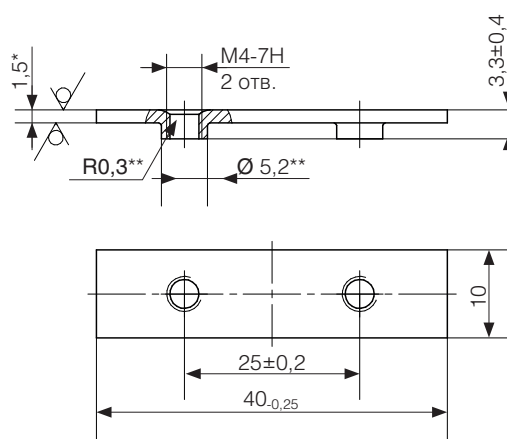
Габаритные, установочные и присоединительные размеры МВЛ 2-2
